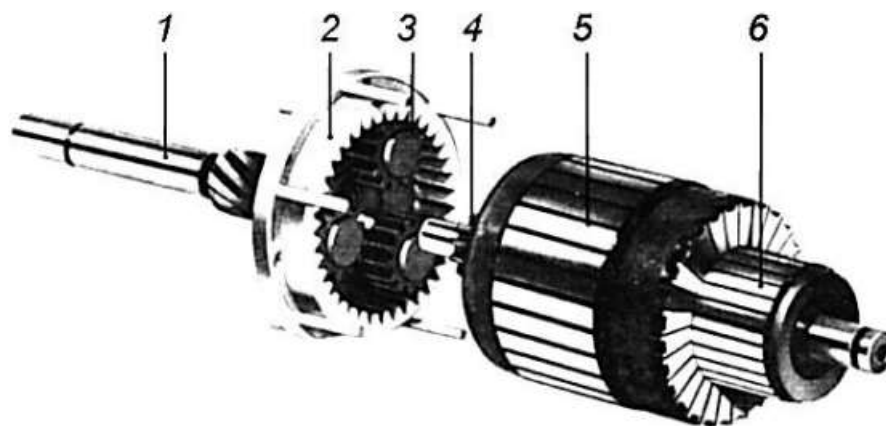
Конструкція стартерного електродвигуна з планетарним редуктором:
